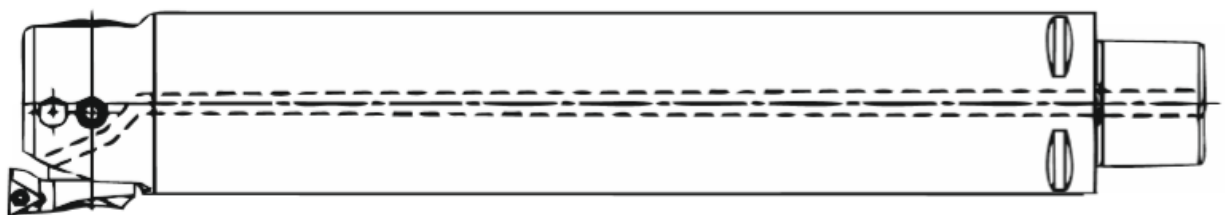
Антивібраційний інструмент “CoroBore 825”
